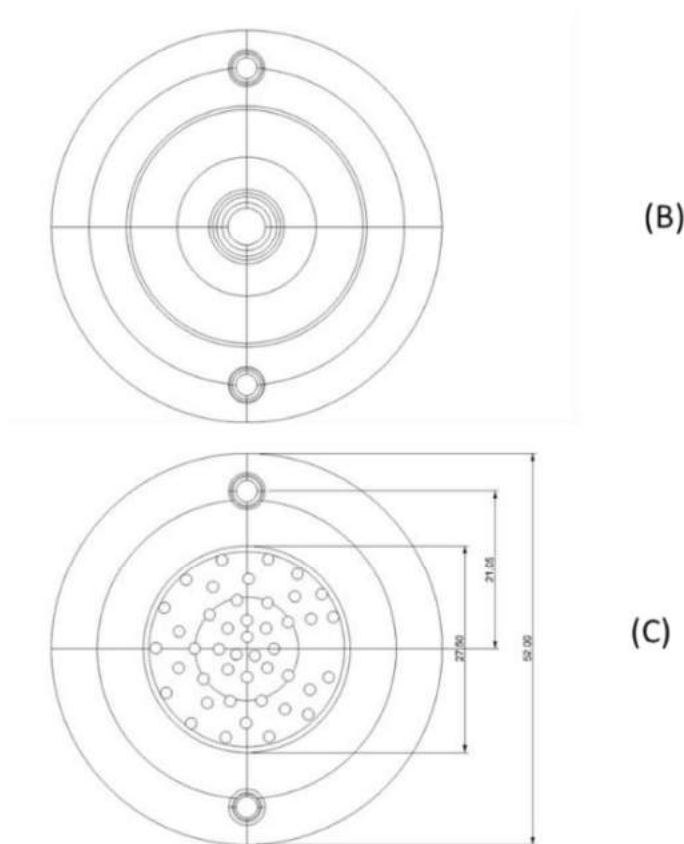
Vista inferior de las piezas torneadas: B) extremo del dispositivo, C) separador de fibras.
